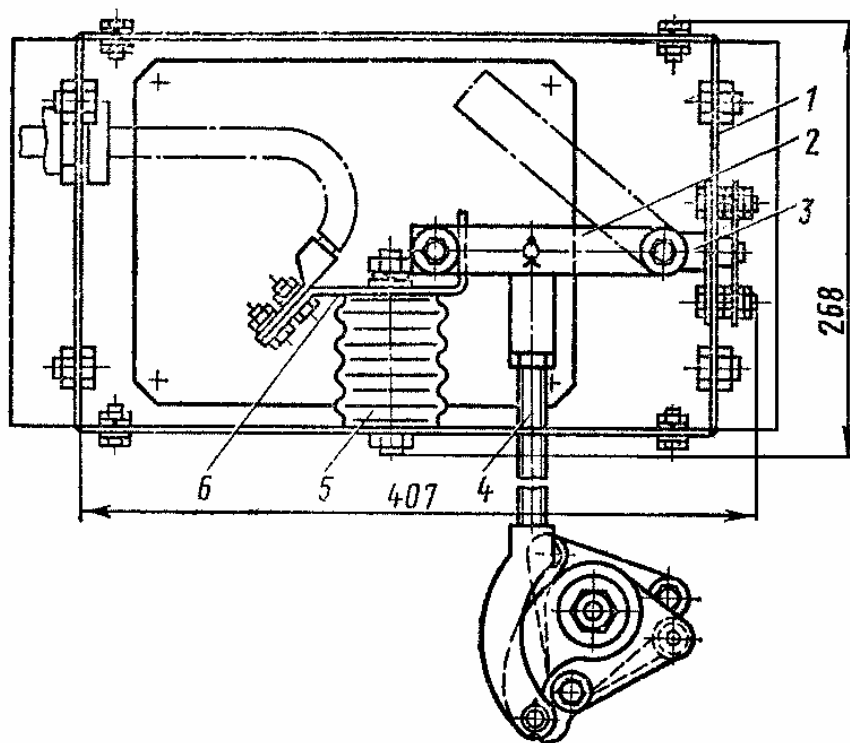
Устройство заземляющего разъединителя РВО-007Т
